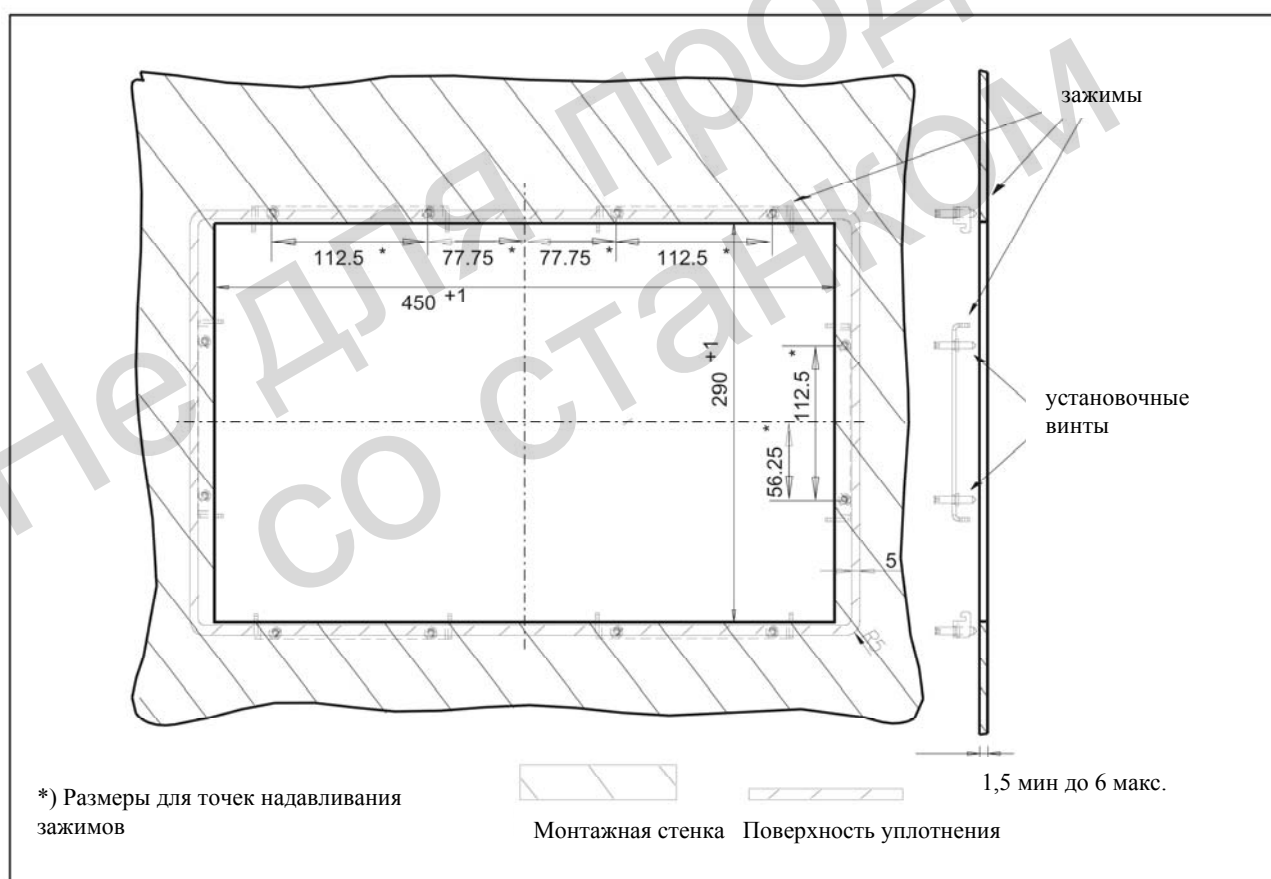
Габаритный чертеж для монтажа панели оператора OP 012
